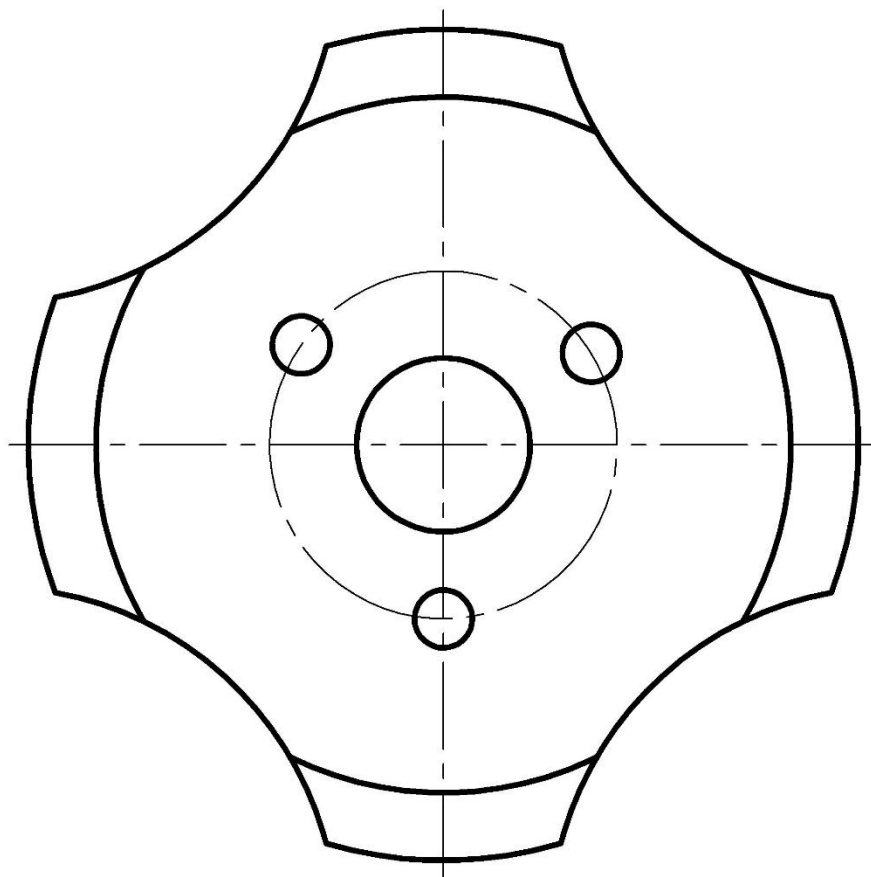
Загальний вигляд конструкції ножа для зрізання соняшнику
